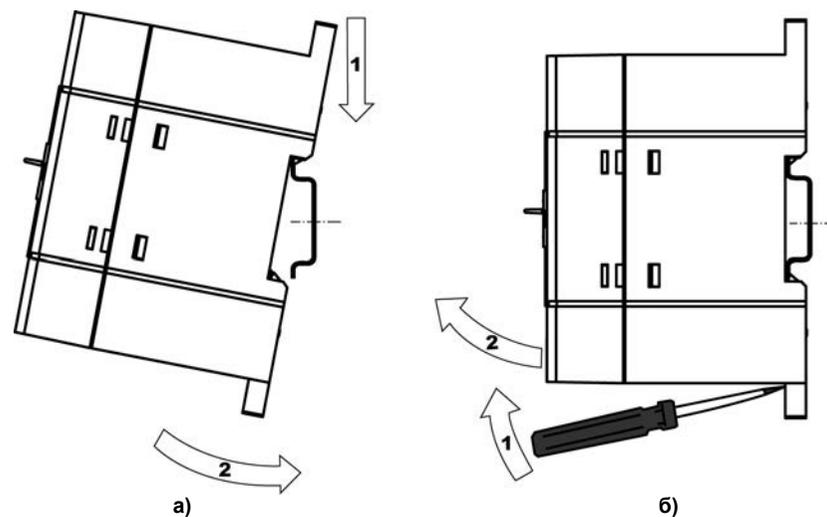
Монтаж контроллера с креплением на DIN-рейку
